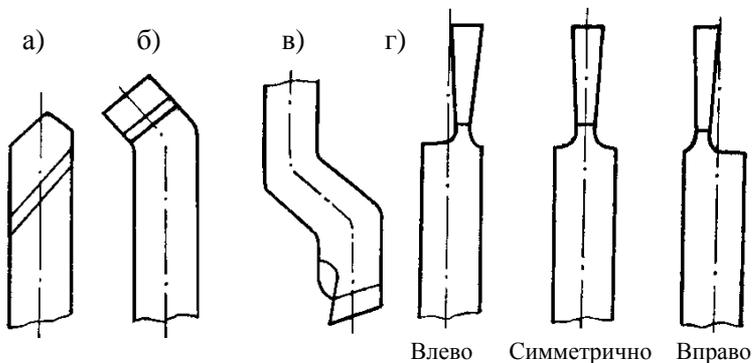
Классификация токарных резцов по конструкции рабочей части
